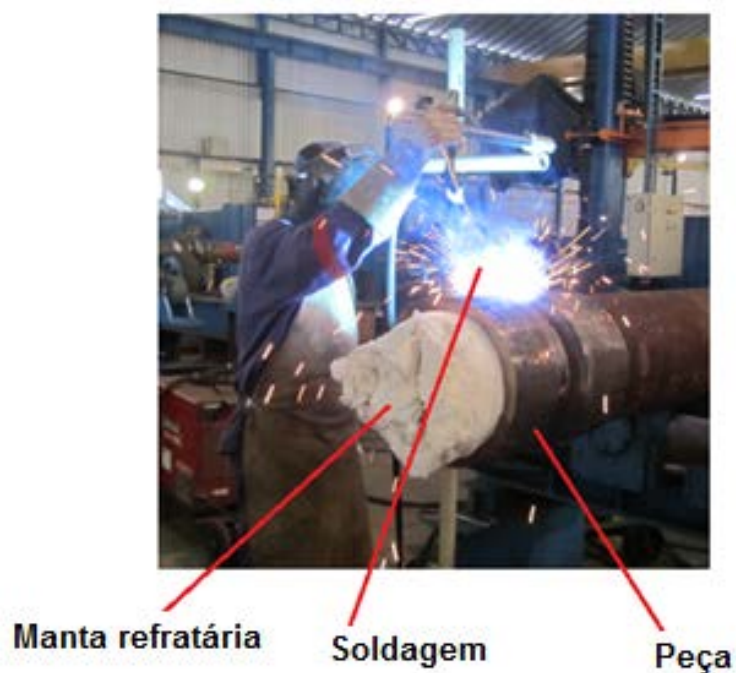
Soldagem da peça de teste pelo processo AT/TIG.
